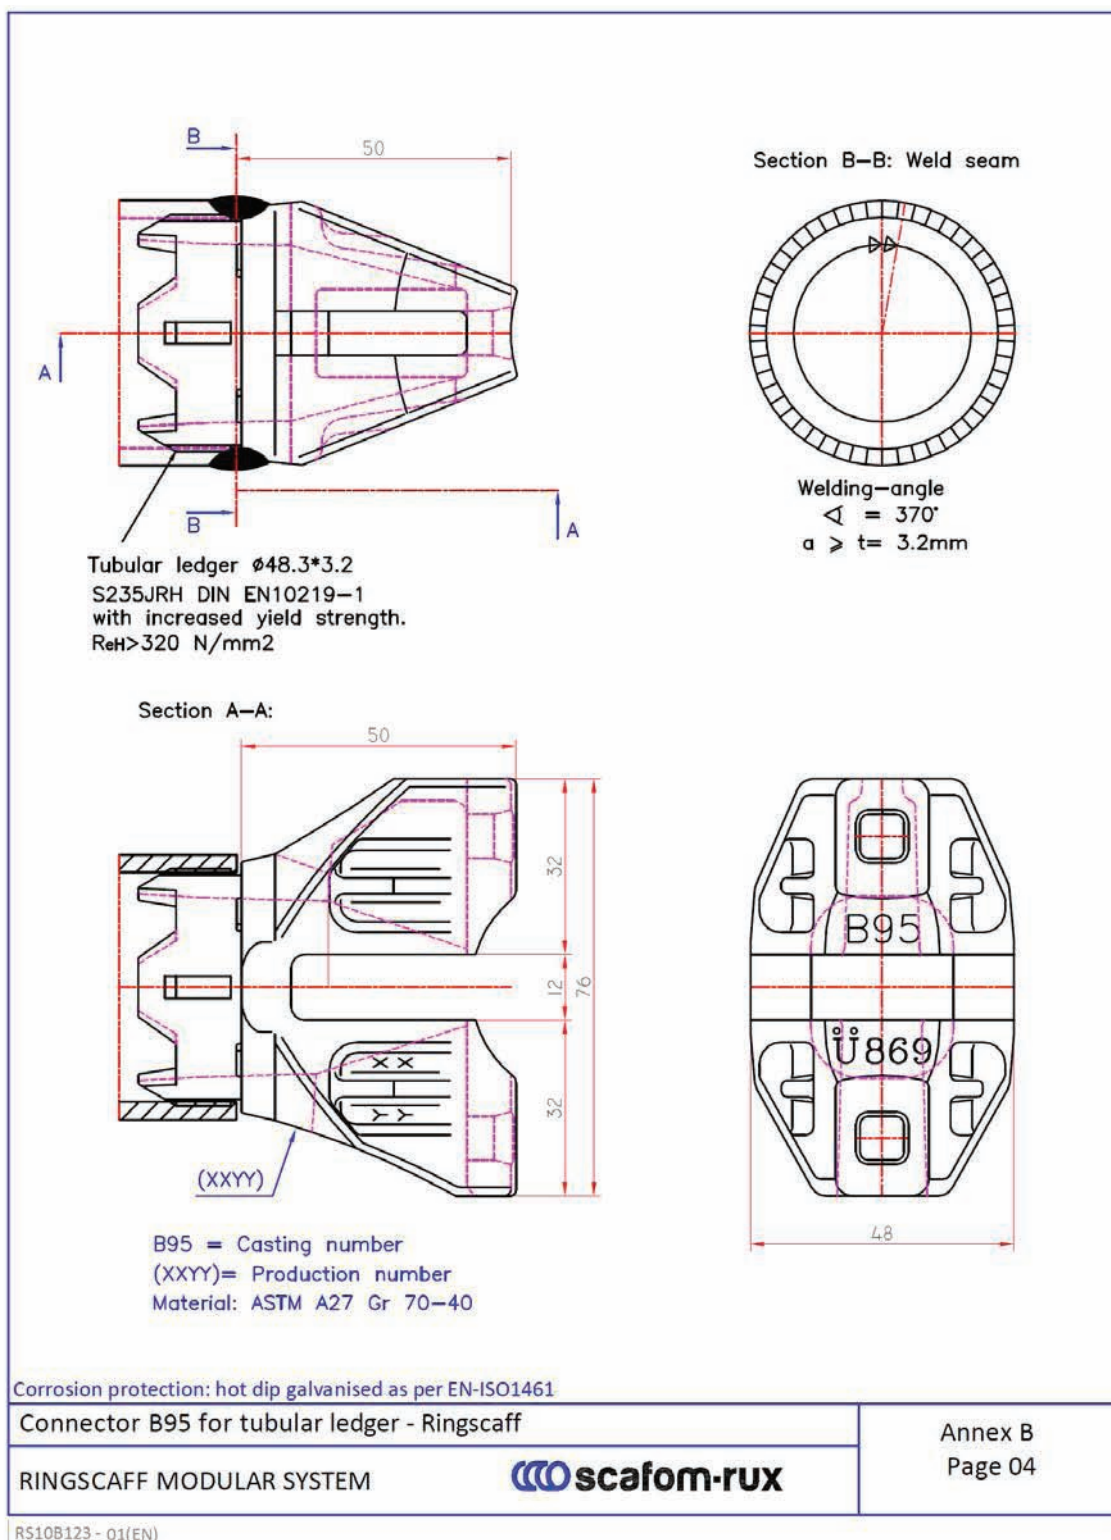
Peça de ligação B95 das travessas com secção tubular
